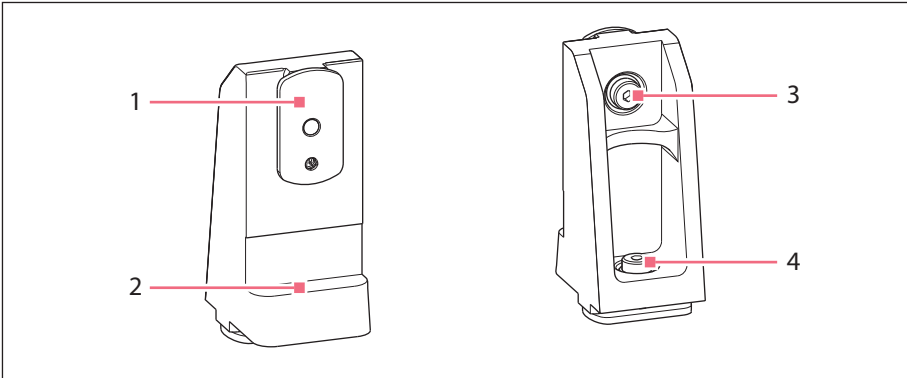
Suporte do módulo Z, lado frontal e lado traseiro
